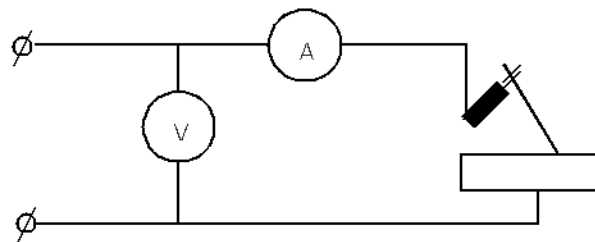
Схема включения измерительных приборов в сварочную цепь
